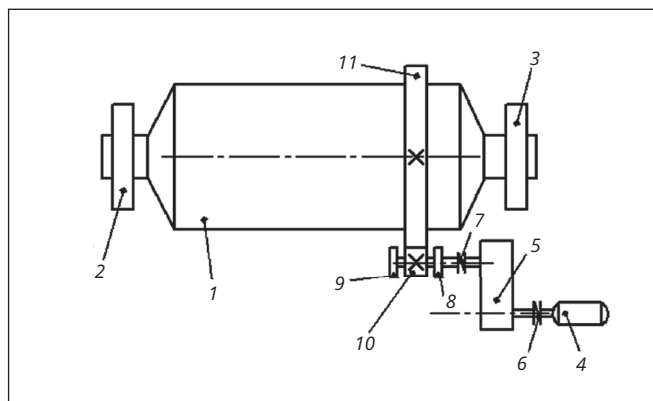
Кинематическая схема шаровой мельницы МШЦ 2,1×3,0: 1 – барабан мельницы; 2 и 3 – подшипниковые опоры барабана; 4 – электродвигатель; 5 – редуктор; 6 – муфта упругая; 7 – муфта зубчатая; 8 и 9 – подшипниковые опоры вала-шестерни; 10 – вал-шестерня; 11 – зубчатый венец
